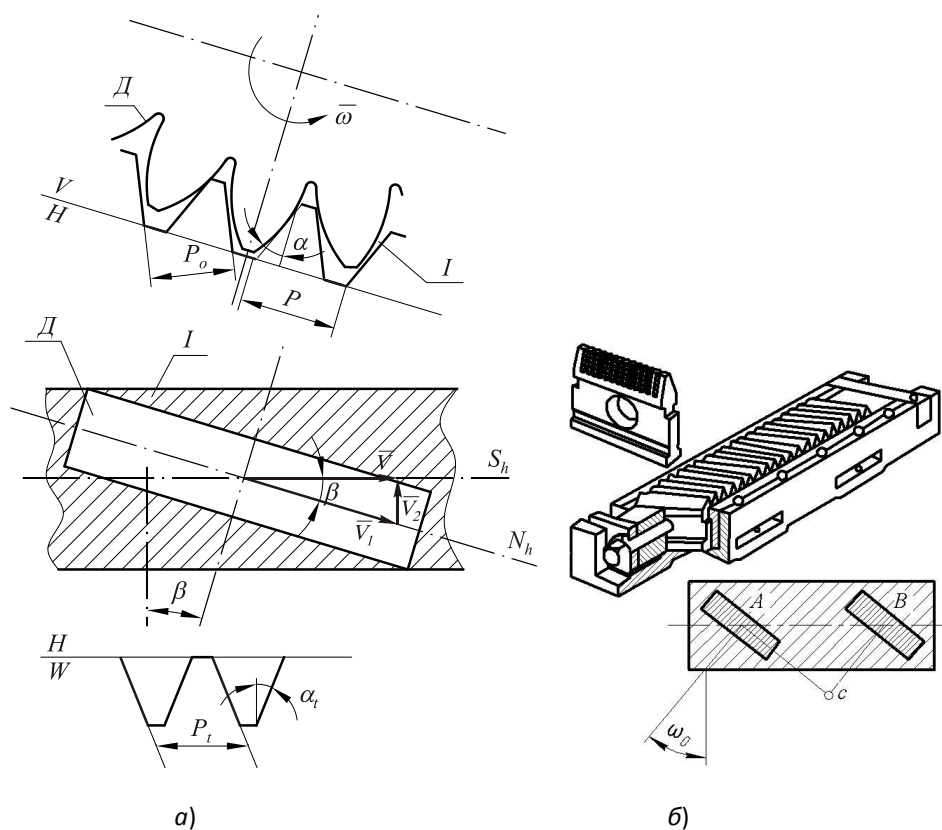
Схема обробки зубчастого колеса шевром-рейкою
